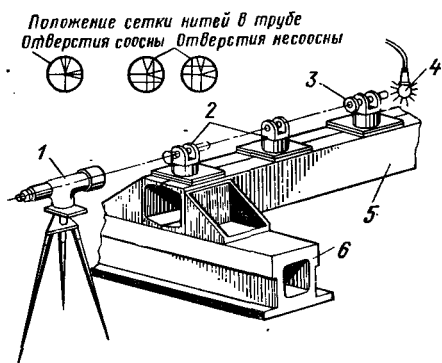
Схема проверки нивелиром соосности фиксаторов приспособления, расположенных на одной горизонтальной оси: 1 — нивелир; 2 — вилки фиксаторов приспособления; 3 — целевой знак; 4 — лампа для освещения целевого знака; 5 — балка приспособления; 6 — основание приспособления
